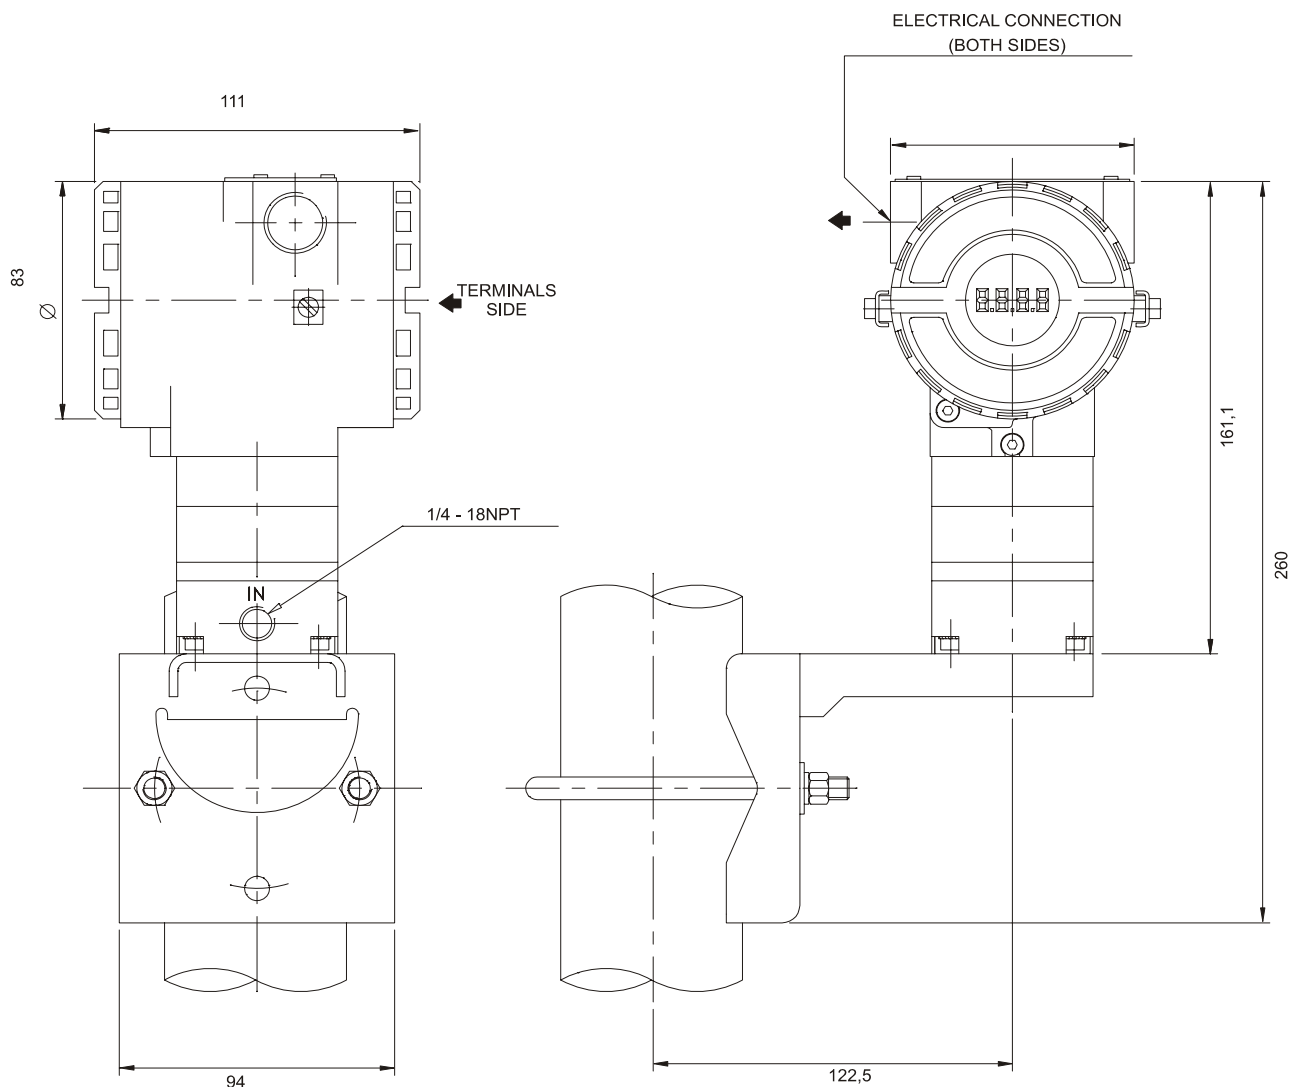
Desenho Dimensional e Posição de Montagem do Conversor
